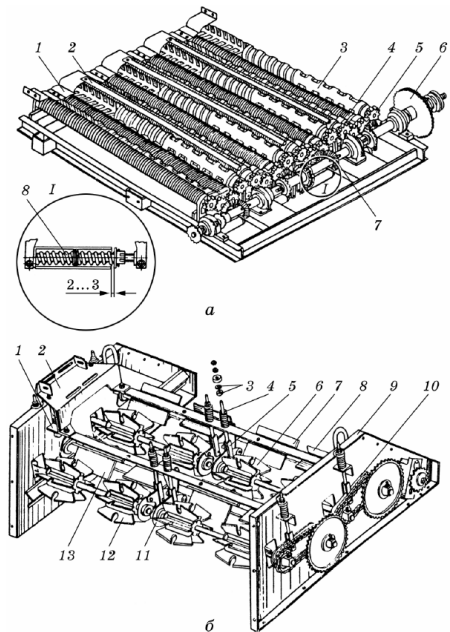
Качановідокремлювальний апарат: 1 – натяжна зірочка; 2 – пружина; 3 – натяжний пристрій; 4 – роздавальна коробка; 5 – полозок; 6 – відривні пластини; 7 – чистик; 8 – вальці; 9 – подавальний ланцюг; 10 – важіль для регулювання зазору між вальцями; 11 – рама [19]
